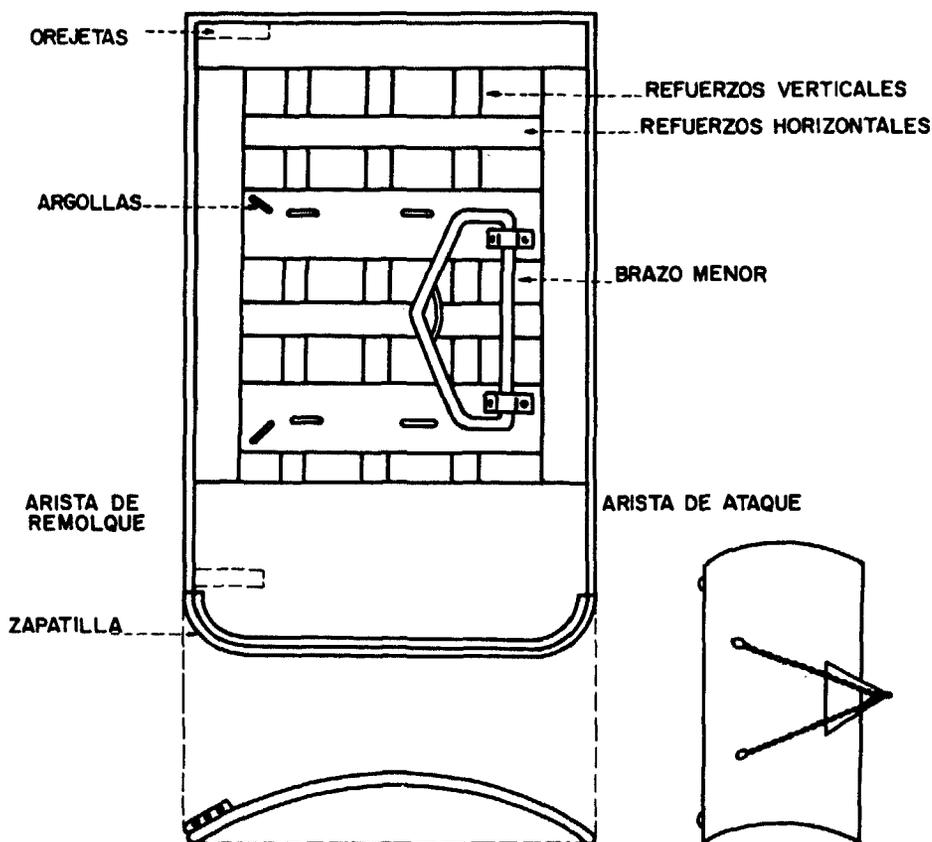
PUERTA DE PERFIL CONCAVO
